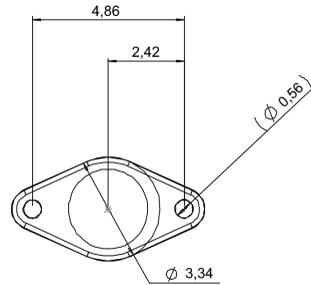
Abmessung der Halterung (in cm) geräteseitig
